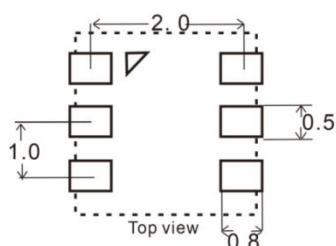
推荐传感器 PCB设计尺寸（单位：mm），外围虚线部分为SMD封装外部尺寸。
